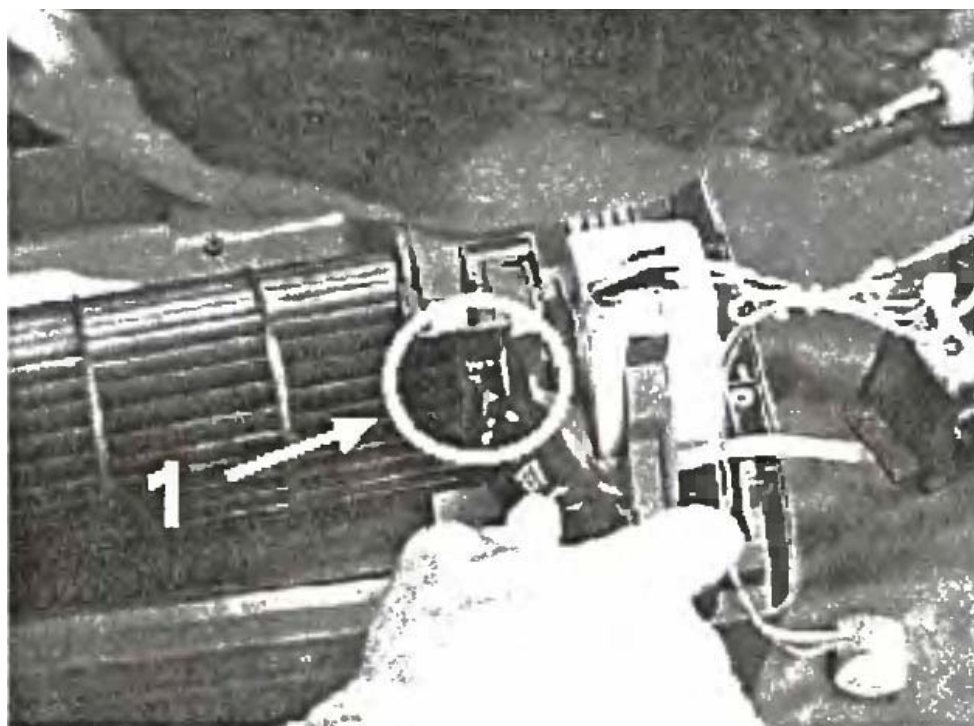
Демонтаж кріплення крильчатки тангенціального вентилятора
